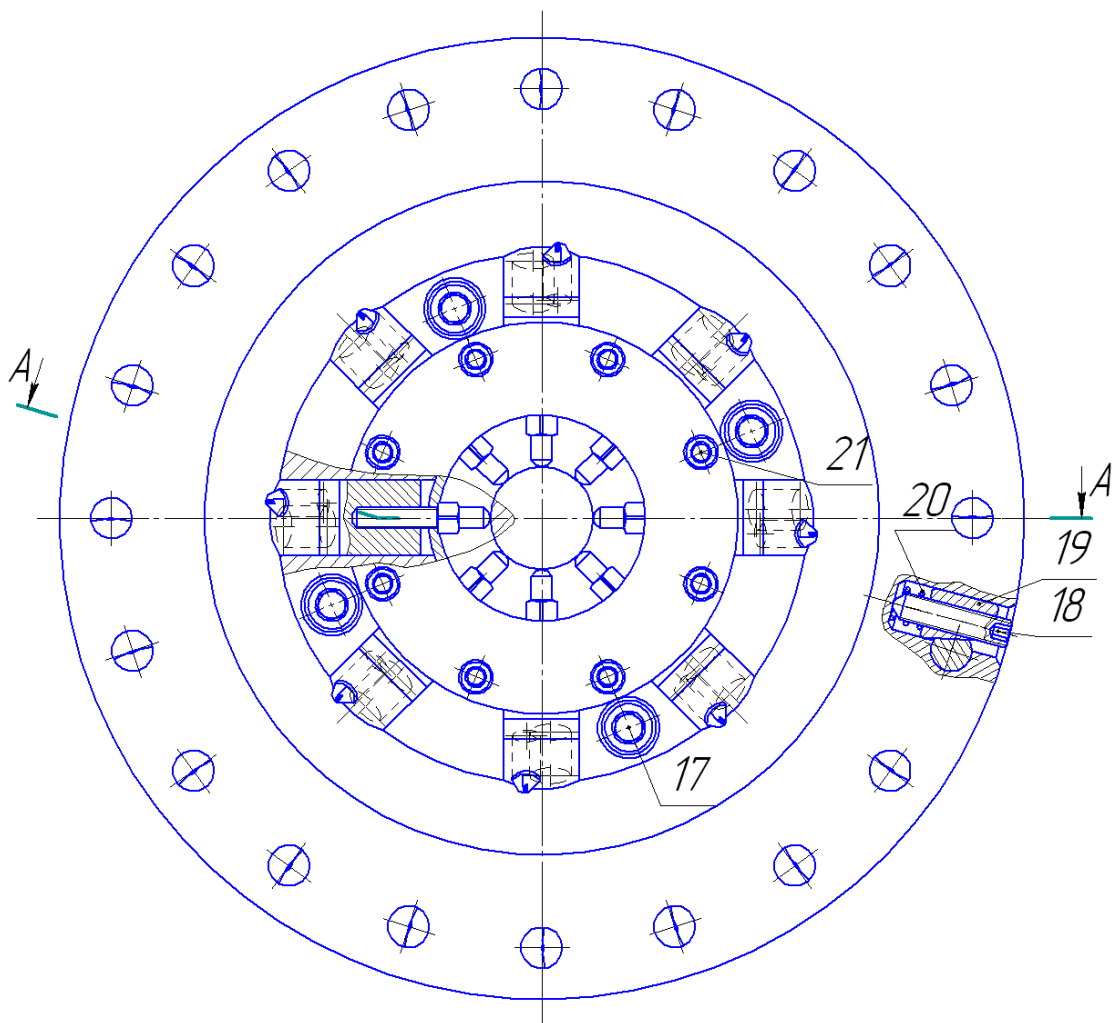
Вид торцевої фрези зі сторони закріплених різальних елементів
